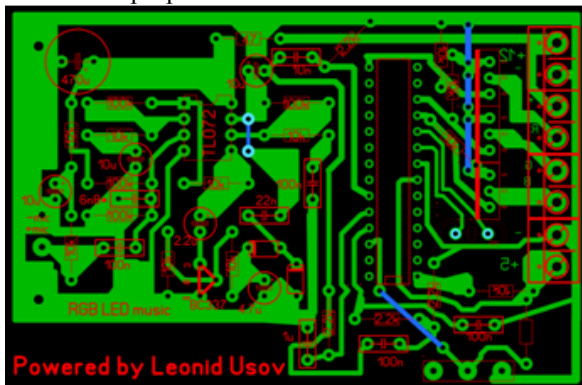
Разводка печатной платы в CAD Sprint Layout 6.
